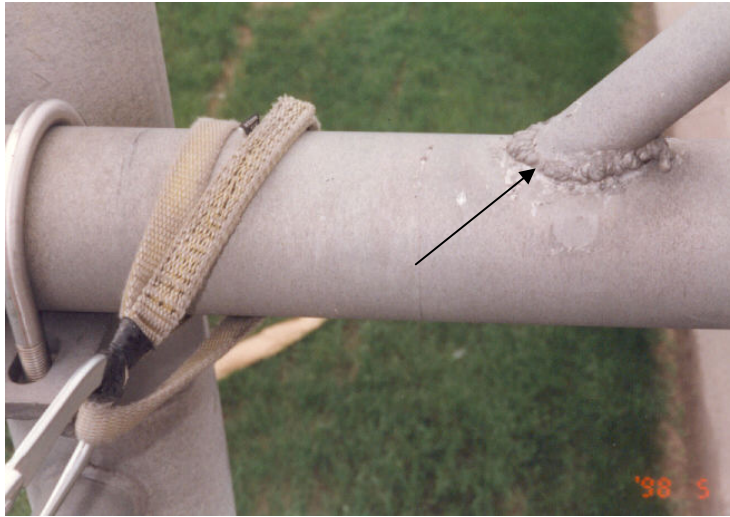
Évaluation du comportement des assemblages soudés
